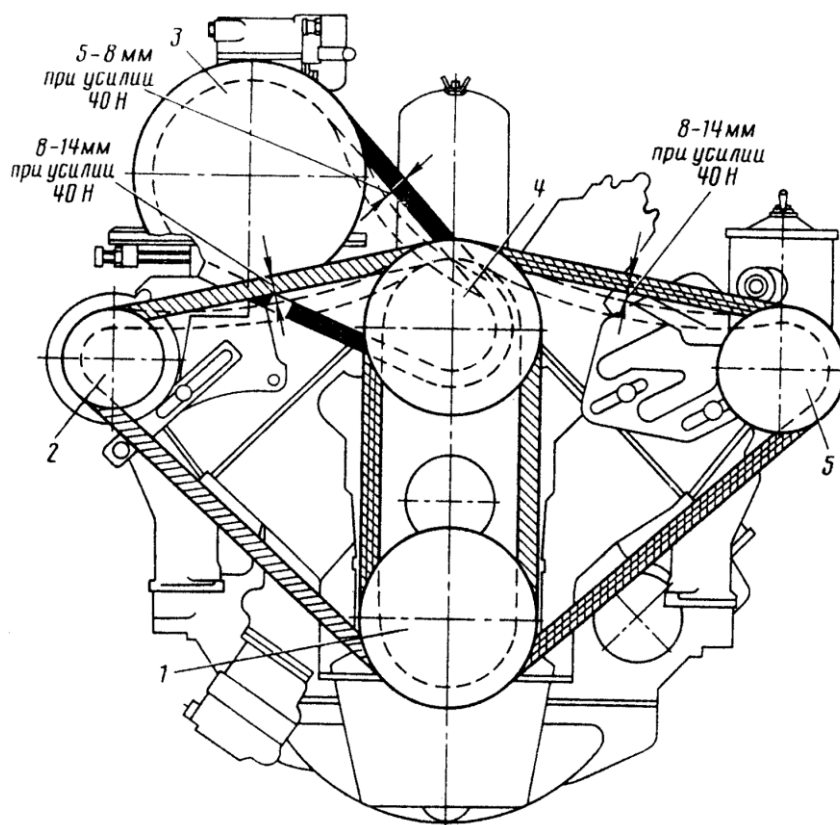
Схема проверки натяжения приводных ремней двигателя ЗиЛ-431410: 1 – шкив коленчатого вала, 2 – шкив генератора, 3 – шкив компрессора, 4 – шкив водяного насоса или вентилятора, 5 – шкив насоса гидроусилителя рулевого привода
